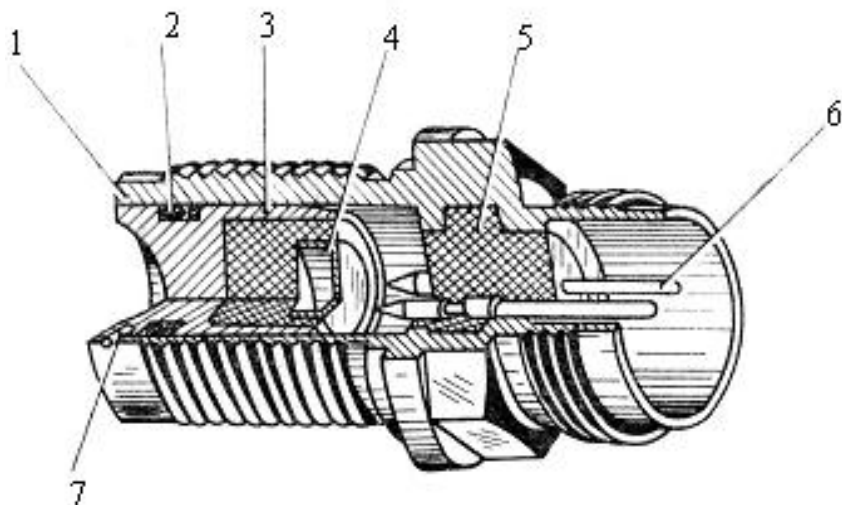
Сигнализатор давления: 1 – корпус; 2 – кольцо; 3 – поршень; 4 – донышко; 5 – изолятор; 6 – контакт; 7 – штифт
